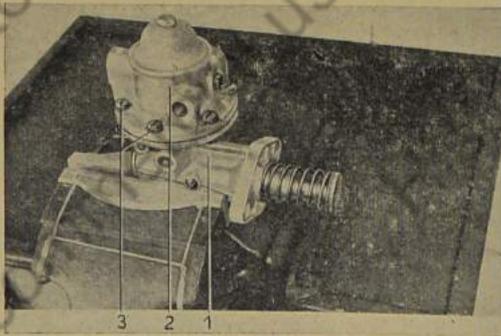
Kraftstoffpumpengehäuse - Oberteil abschrauben
